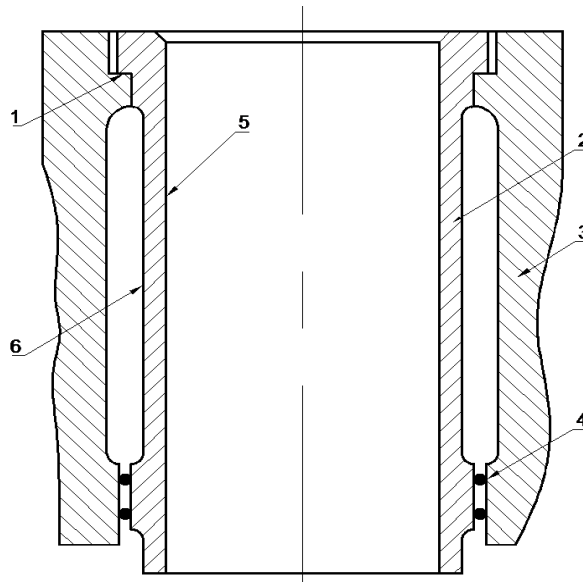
Положение цилиндрической втулки в блоке двигателя:
